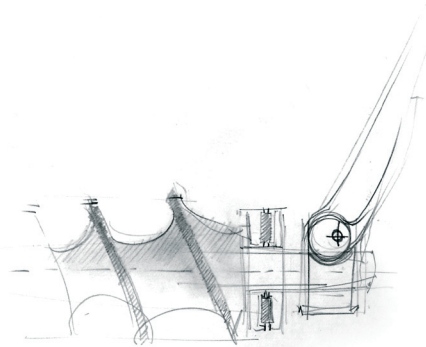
Nákres řešení s převodem do pravého úhlu pro vertikální i horizontální koncept strojku
